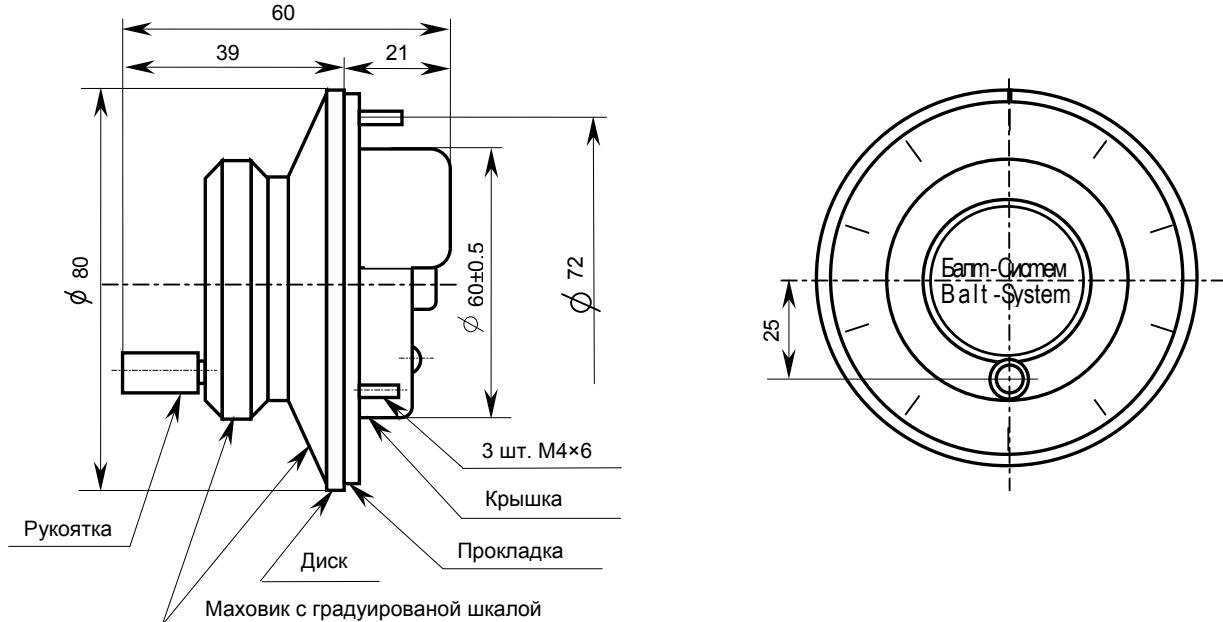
Габаритные размеры штурвала LGF-12-003B-100
